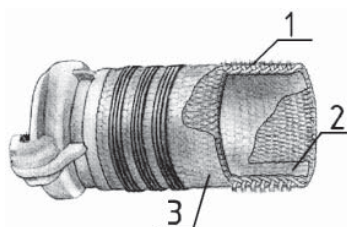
Конструкция напорного рукава с двусторонним покрытием
